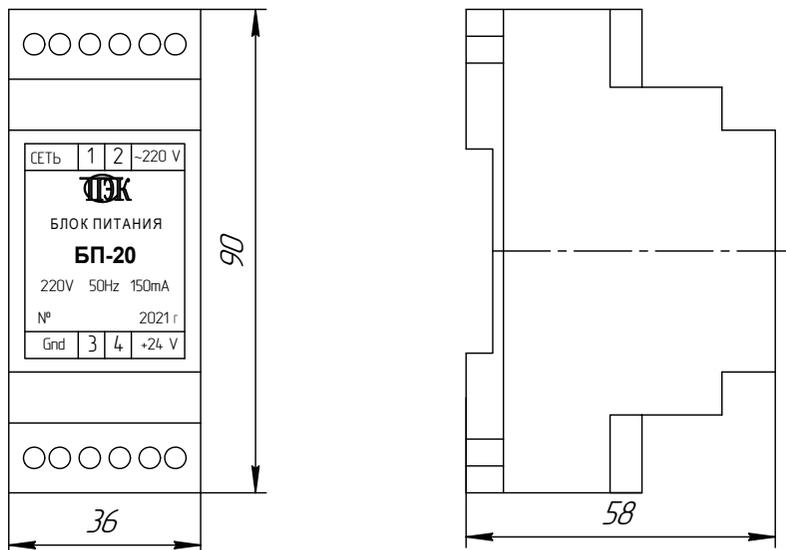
Габаритные размеры блока БП-20 (на DIN-рейке)
